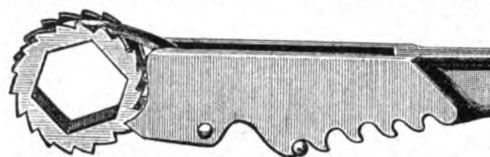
„Rapid“-Schraubenschlüssel mit eingefestigter Nut.
